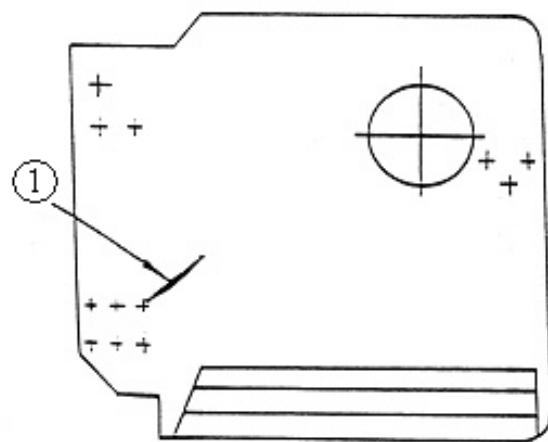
Дефект площадки откидной, ремонтируемы сваркой
